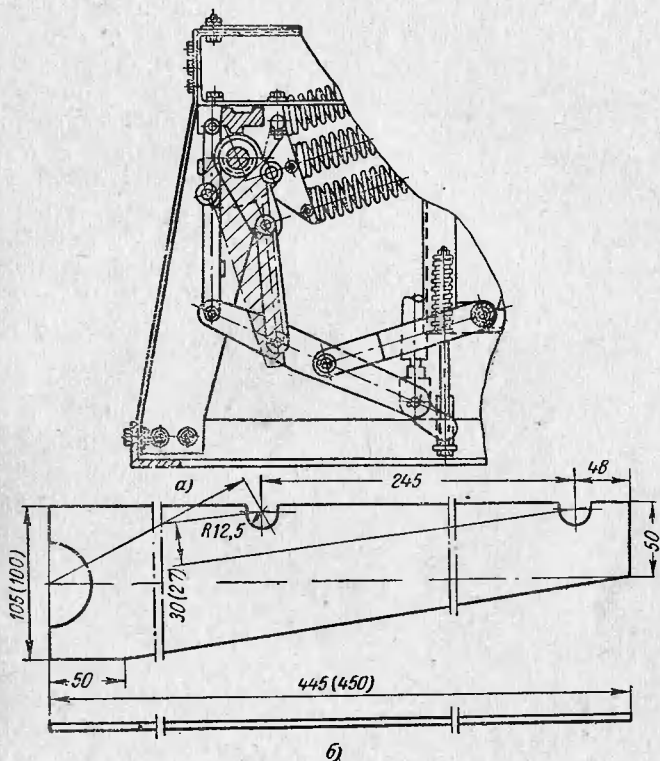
Проверка шаблоном приводного механизма выключателя типа МГ.
